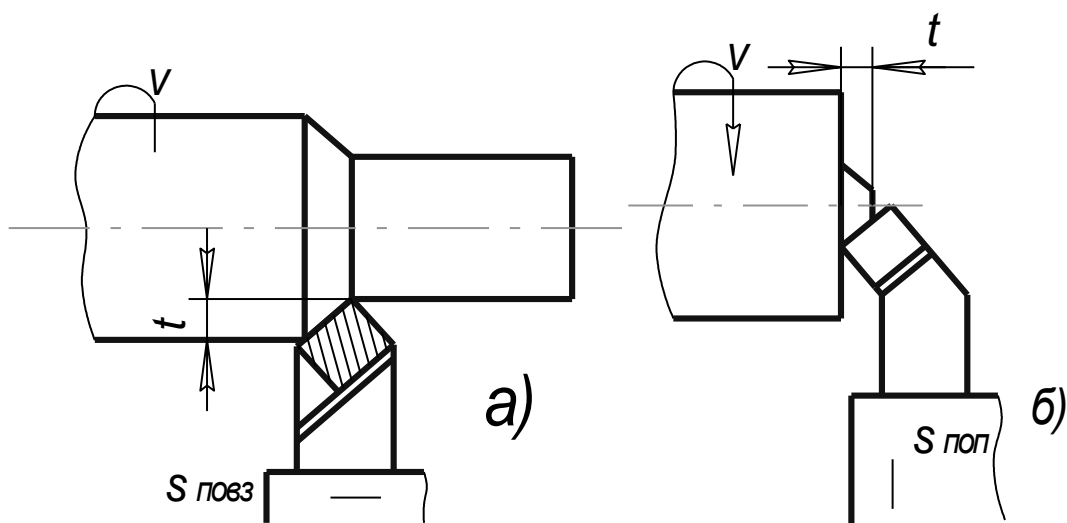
Схеми робочих рухів при токарній обробці:
